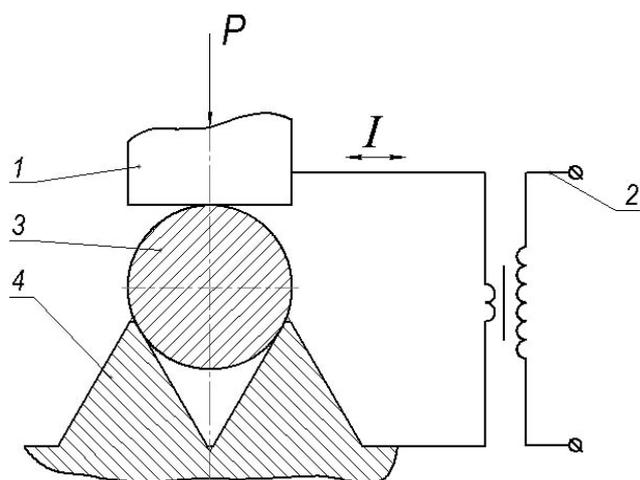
Электроконтактная приварка проволоки: 1 – электрод; 2 – сварочный трансформатор; 3 – материал (проволока); 4 – витки резьбы
